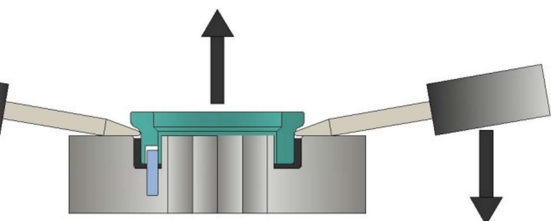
Dichtung aus dem Rotor ausbauen
